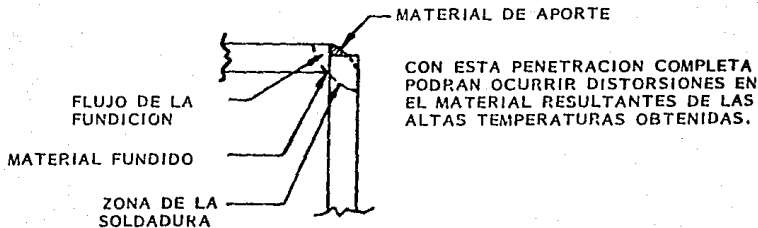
SOLDADURA CON PENETRACION
